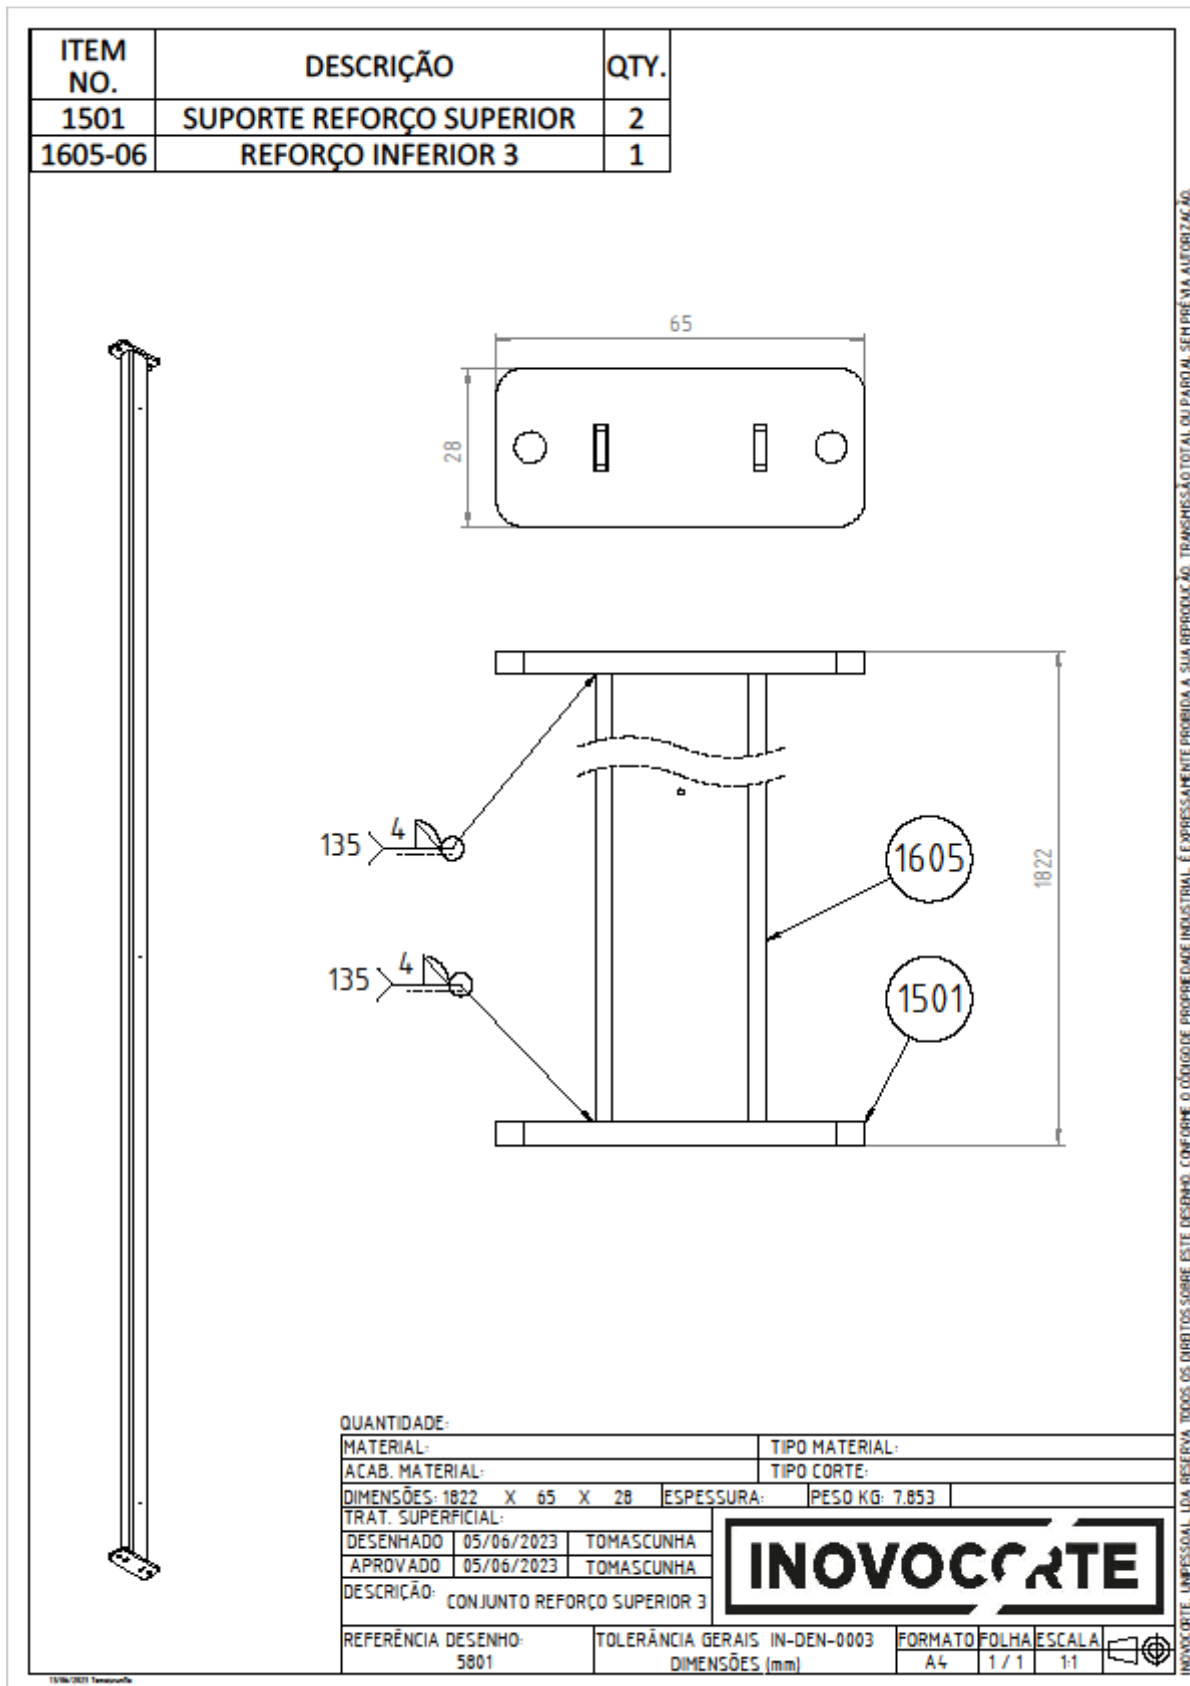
Desenho técnico do conjunto reforço superior 3 (5801).
